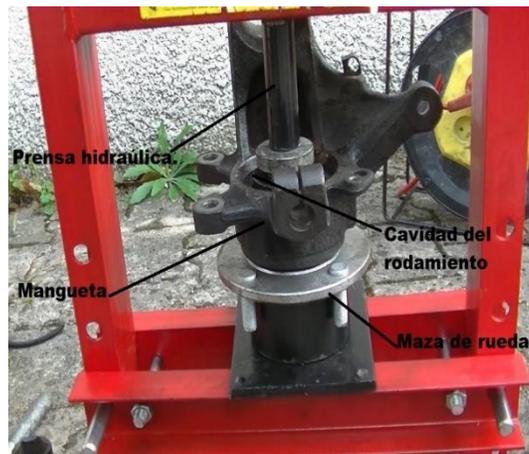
Prensa hidráulica que se utiliza para cambio de rodamientos y bujes.
